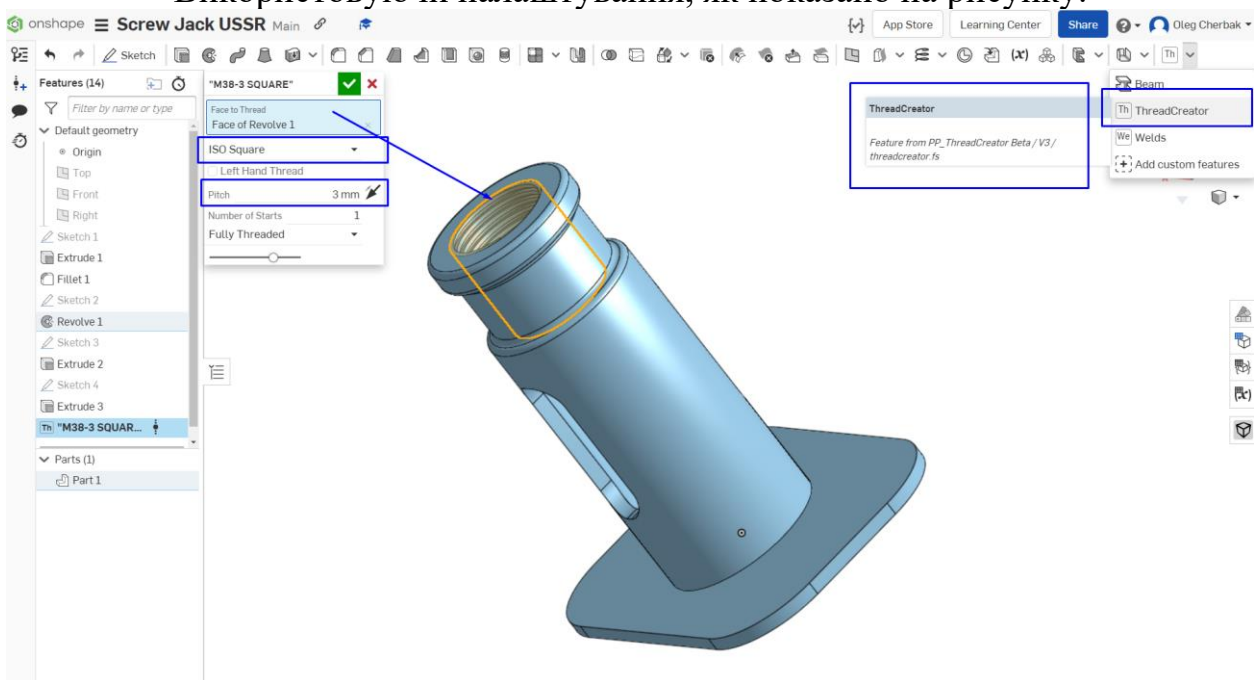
За допомогою різьбонарізного інструменту зробіть різьбу на верхній частині корпусу.
